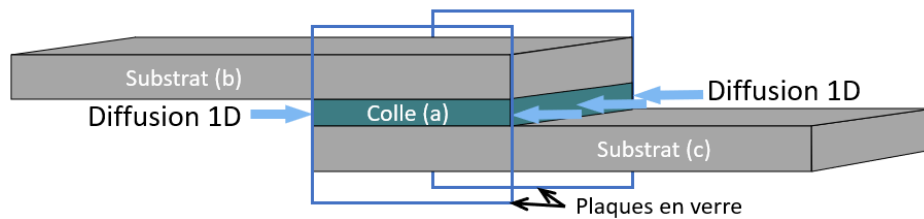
Assemblage des échantillons de joints à simple recouvrement
